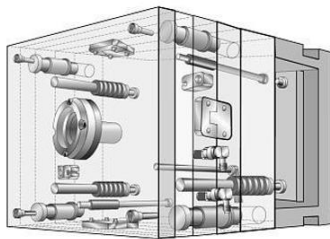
Molde de injeção (fonte: Campo, 2006).
